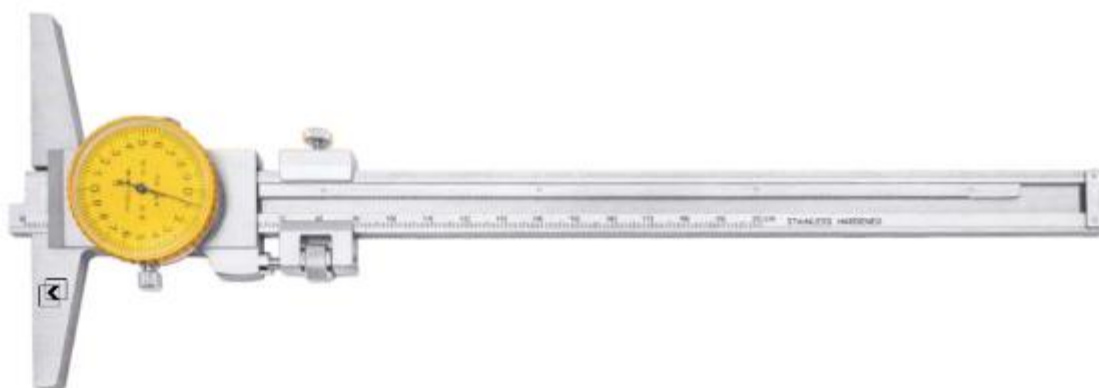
Общий вид штангенглубиномеров модели ШГК
